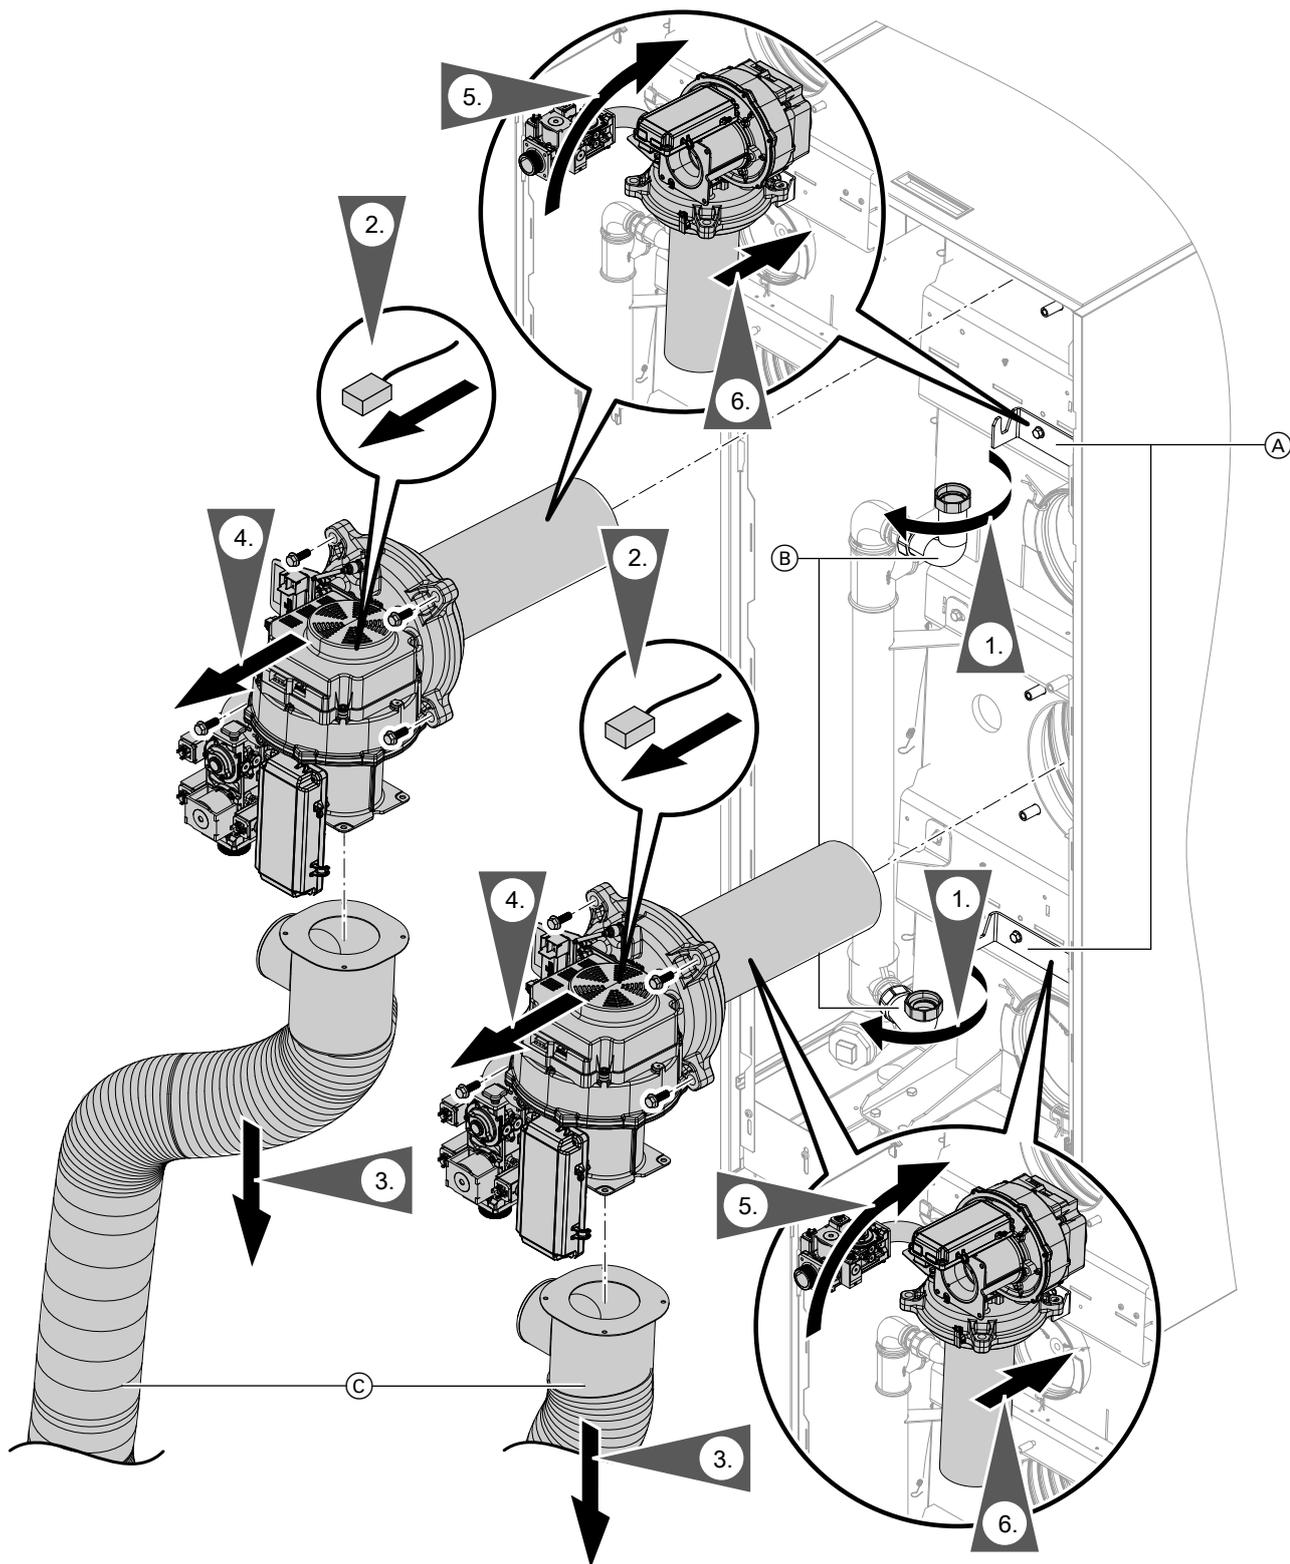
Beispiel Brennermodul 300, Wärmeerzeuger CI3 640 mit RLU-Set
